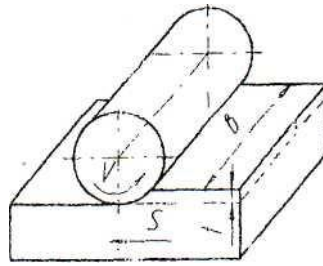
Елементи режиму різання при фрезеруванні
